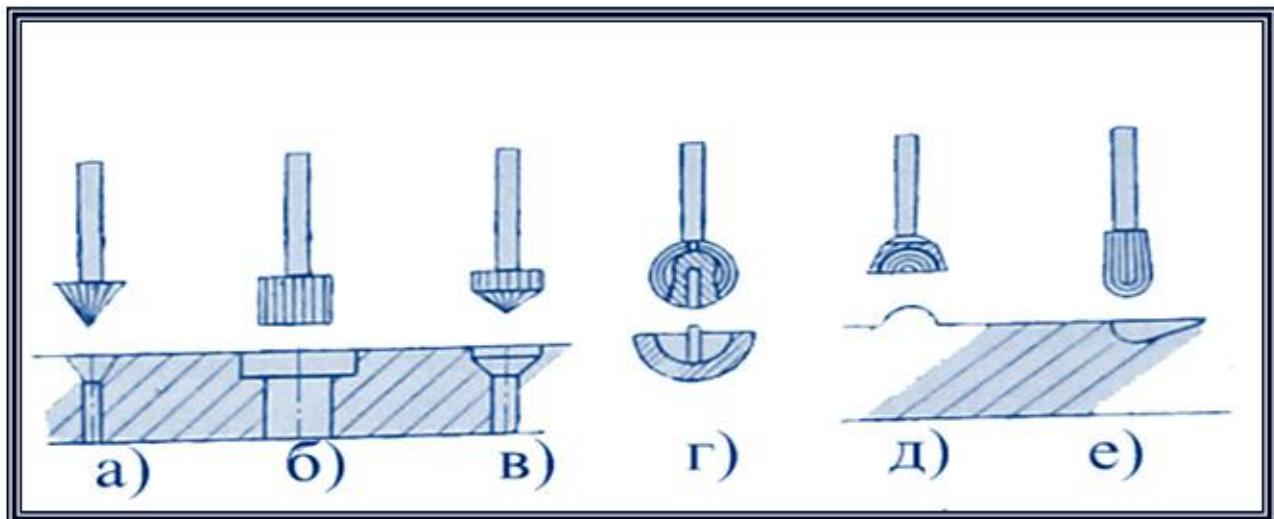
Фрези «бори»: а) конічна; б) циліндрично-торцева; в) комбінована гостра циліндрична; г) кульова; д) плоска сферична; е) фасонна
